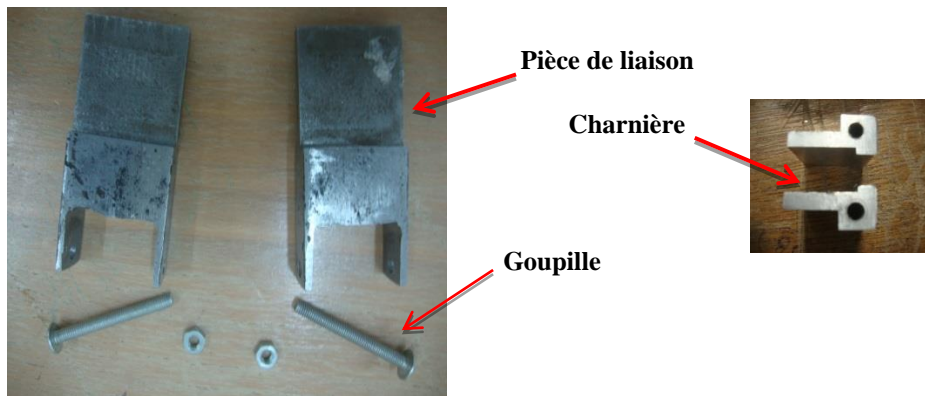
Dispositif de fixation de l'éprouvette à la machine.
